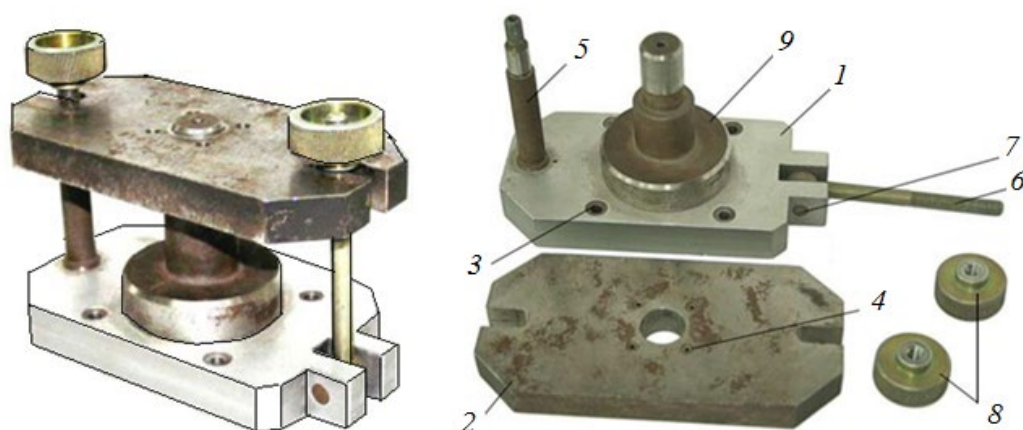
Пример кантующегося кондуктора для сверления отверстий на двух торцах втулки:
